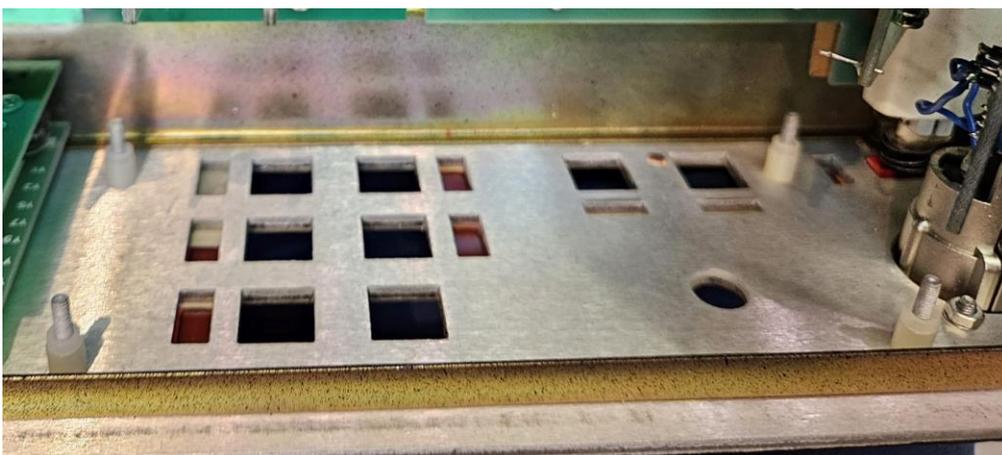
in diese Ausschnitte müssen die Tasten nachher passen!
